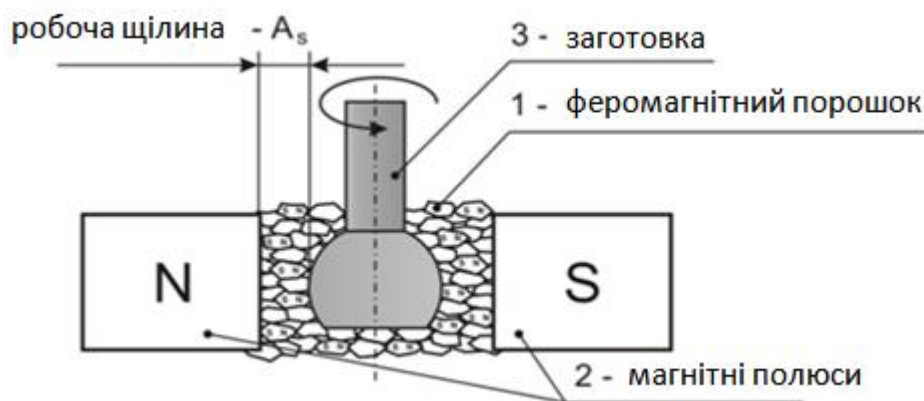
Принципова схема для МАО обертОВО-симетричних заготовок
